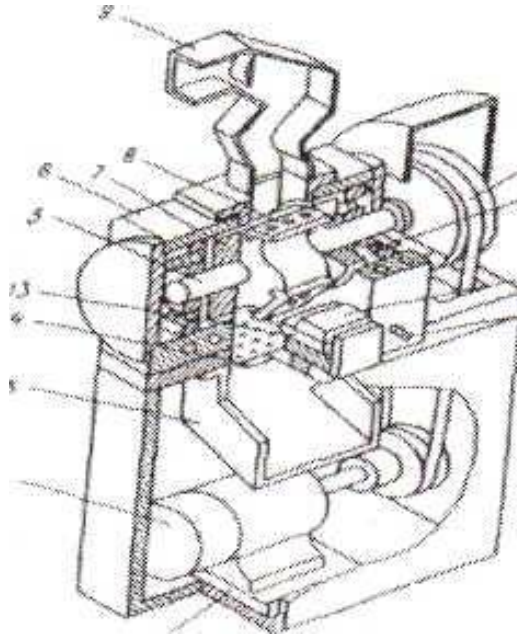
Загальний вигляд роторно-ножового дробильного агрегату
